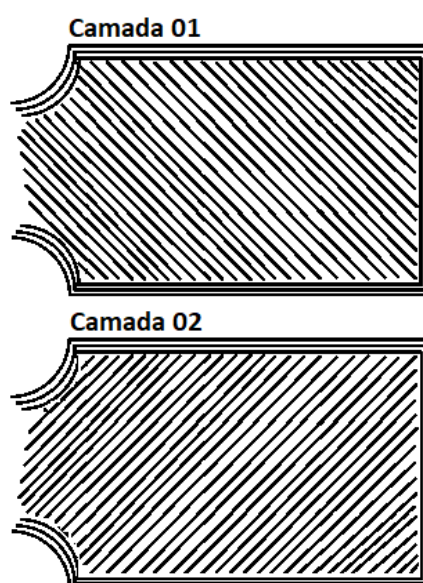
Construção das camadas da amostra (Fonte: O próprio autor)
